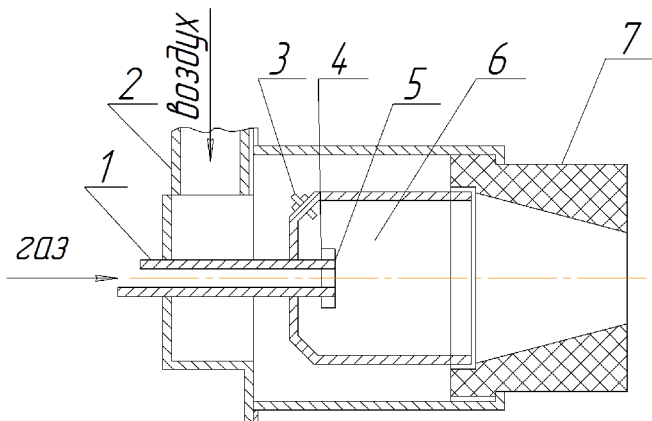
Скоростная газовая горелка: 1 — патрубок для подачи газа; 2 — патрубок для подачи воздуха; 3 — свеча зажигания; 4 — газовое сопло; 5— стабилизатор горения; 6 — камера сгорания; 7 — огнеупорное сопло
